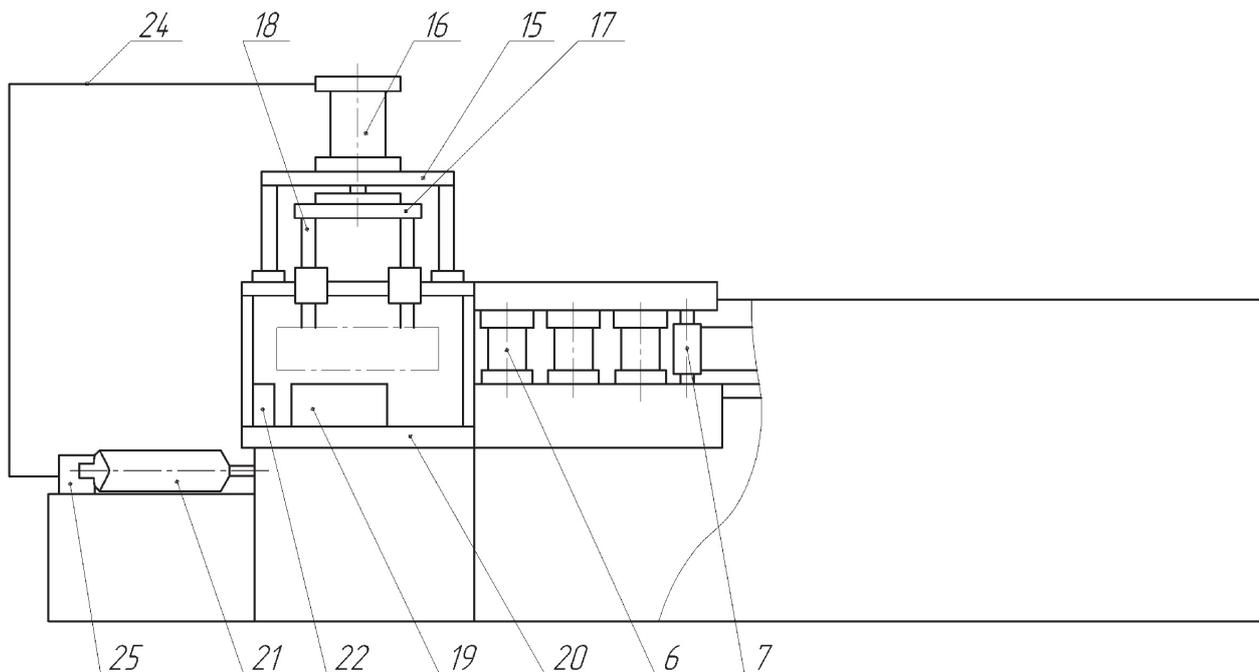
Принципиальная схема стана для прокатки заготовок малолитровых рессор автомобилей МАЗ (вид сбоку)
